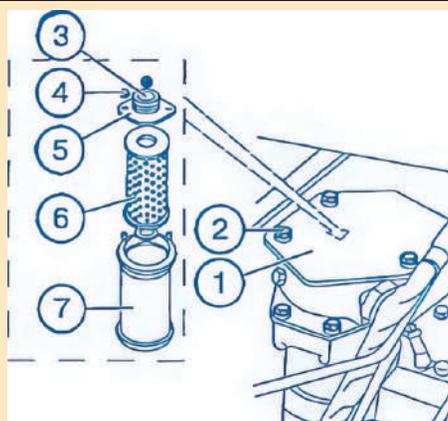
Заміна оливного фільтра в корпусі гідроагрегатів
